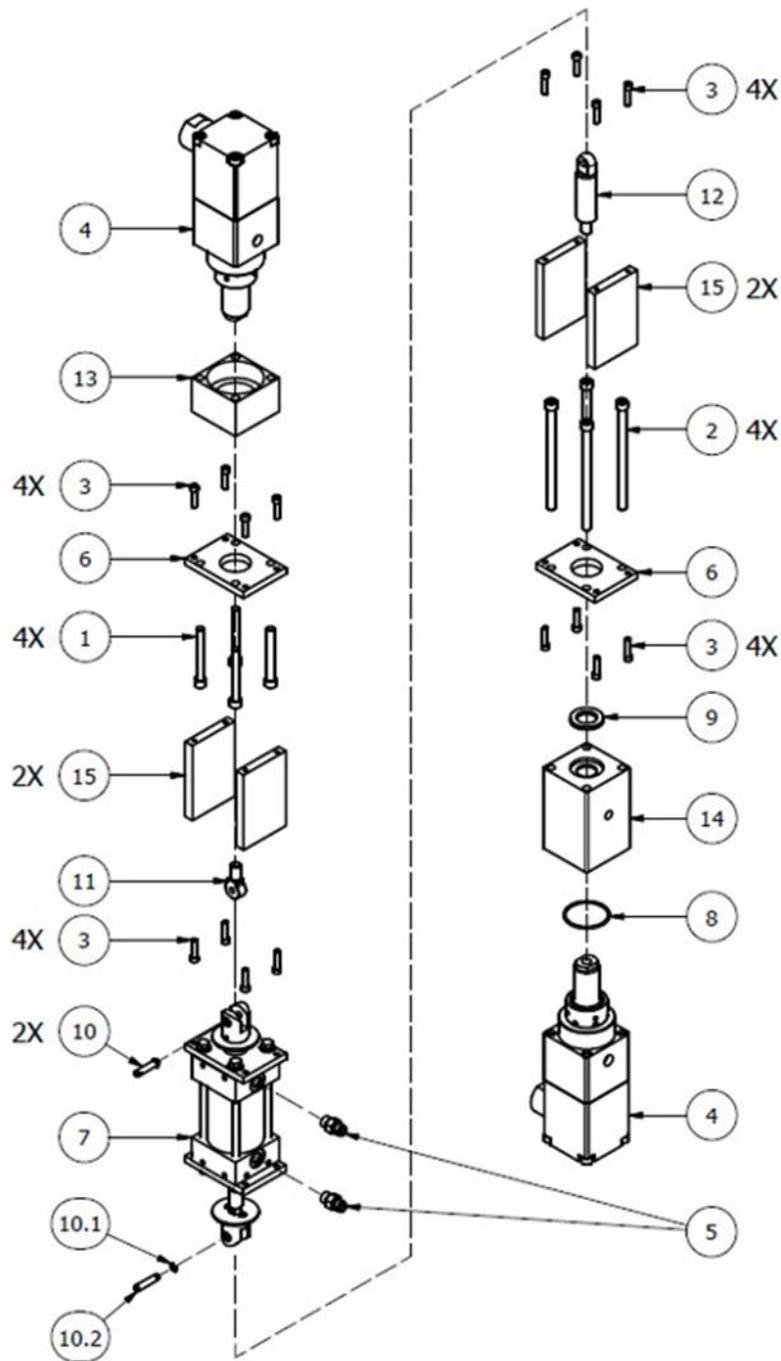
Ensamblaje de la línea de bomba (PL-9)
